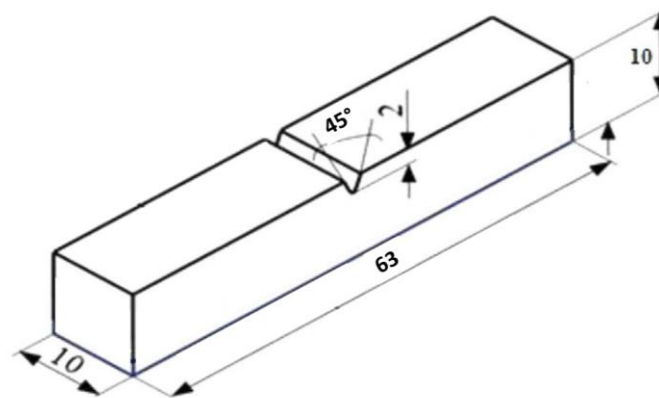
Dimensiones del espécimen para ensayo de impacto Charpy expresado en mm.
